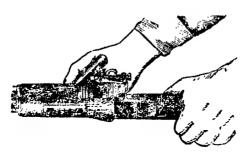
Поворот замыкателя газовой трубки с помощью пенала принадлеж-
